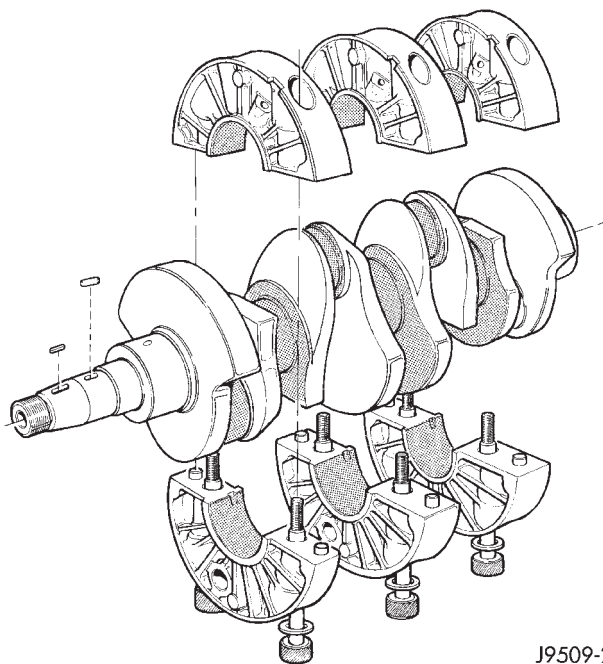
Ensemble du vilebrequin et des coussinets de palier
